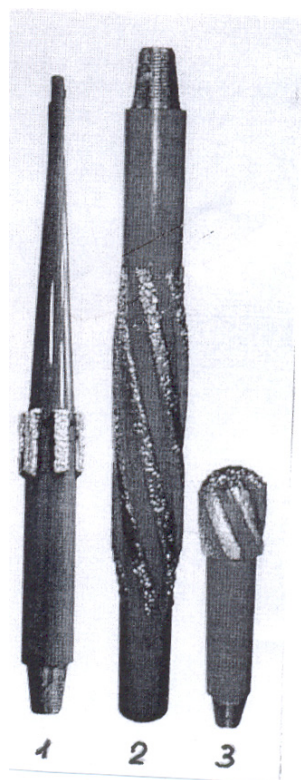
Комплект фрезеров для зарезки боковых стволов
